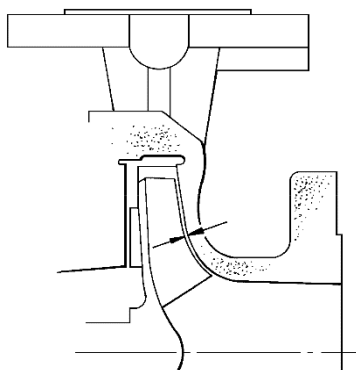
(Установка зазора для рабочего колеса открытого типа)
